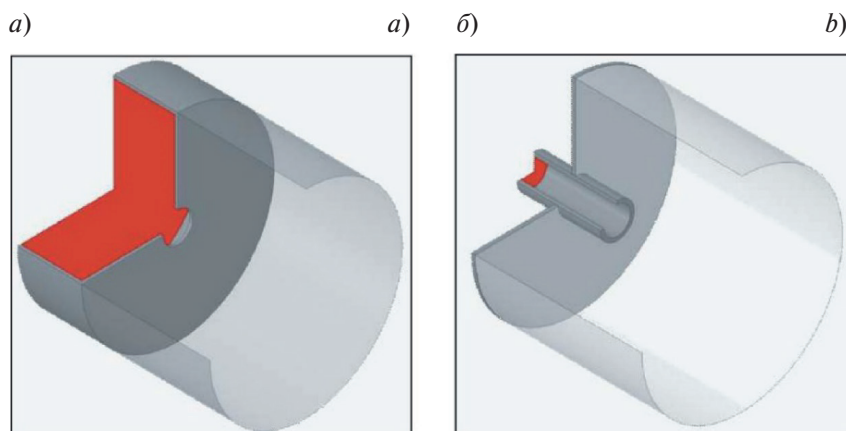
Генераторы вихревых колец в виде стенки с отверстием (а) и цилиндрической трубки (б)
